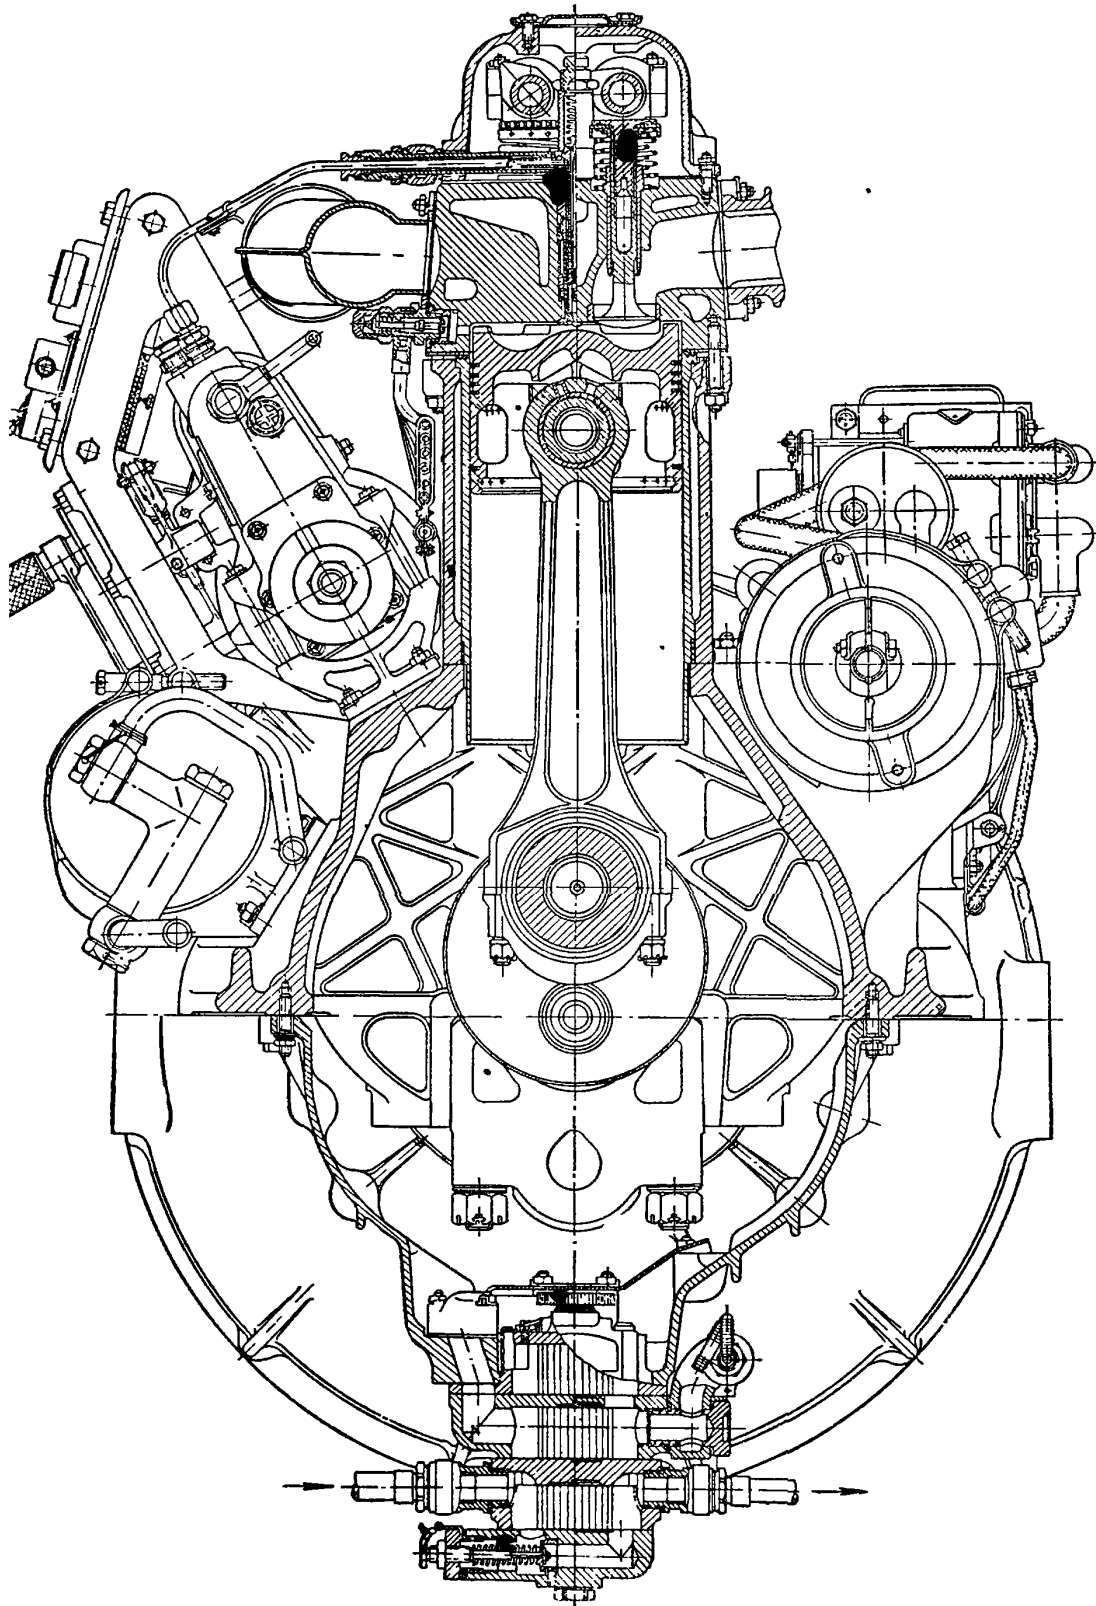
Разрез по механизмам привода и анкерным шпилькам двигателя Д-12.
